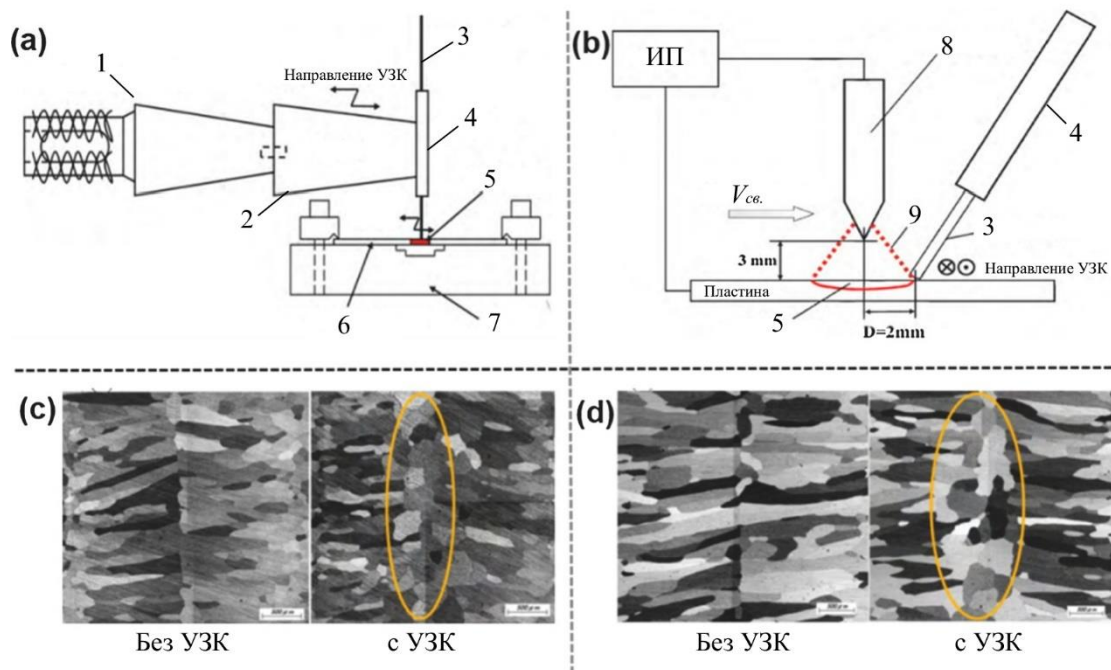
Схема устройства (а) и расположения присадочной проволоки (b) и микроструктуры сварных соединений (с, d) [46]: 1 – ультразвуковой преобразователь; 2 – волновод; 3 – присадочная проволока; 4 – направляющая трубка; 5 – сварочная ванна; 6 – пластина; 7 – сварочный стол; 8 – неплавящийся электрод; 9 – дуга
